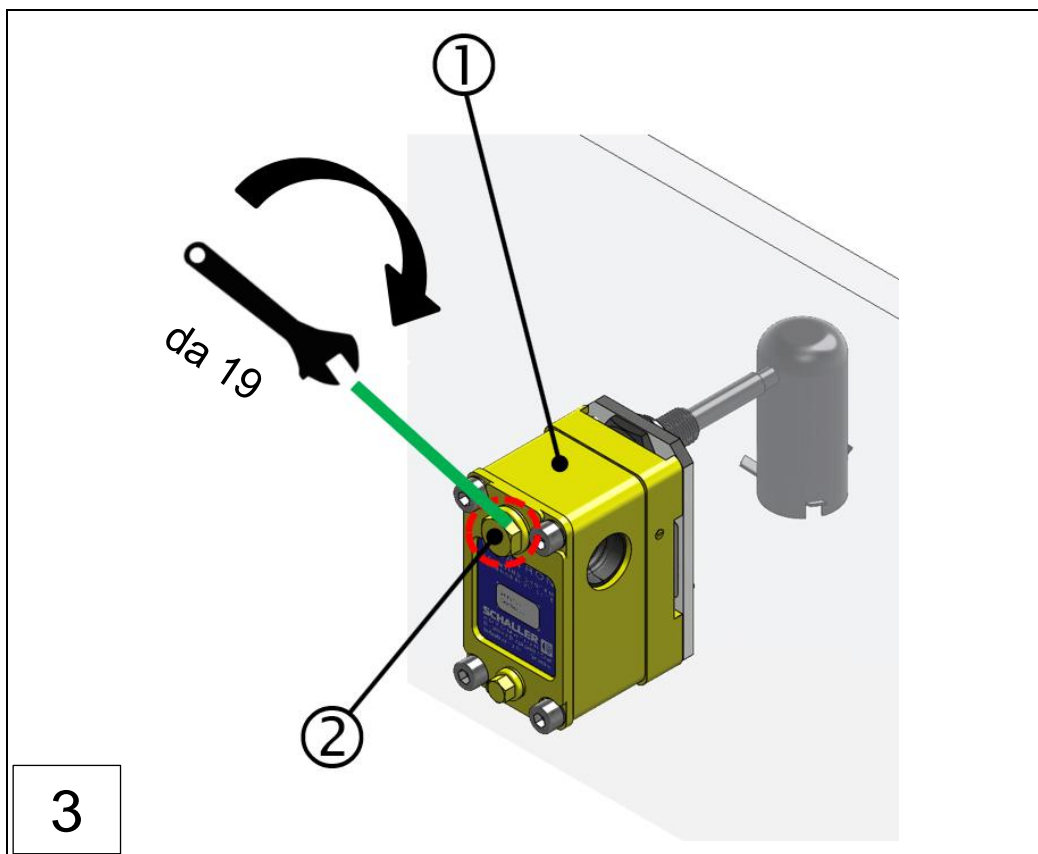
Test in fabbrica con generatore di fumo (passaggi 1 - 3)
